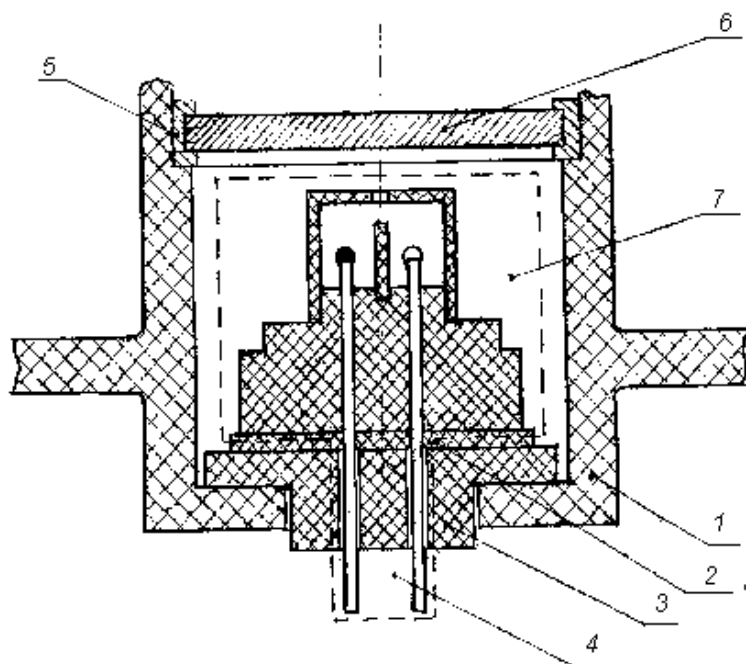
Конструкция датчика с дополнительным газодиффузионным фильтром смонтированного в корпусе изделия: 1 – корпус изделия; 2 – амортизатор; 3 - втулка; 4 – датчик в сборе; 5 – кассета; 6 – фильтрэлемент; 7 – полость.
